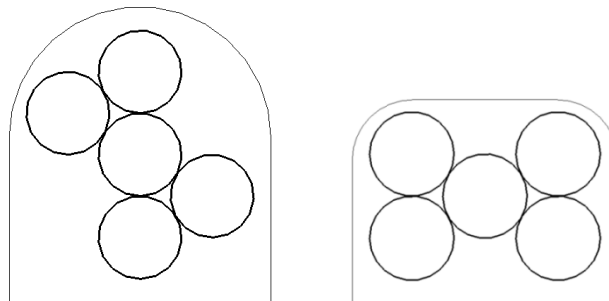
(Izquierda) posición engranajes diferencial versión preliminar. (Derecha) posición engranajes diferencial versión definitiva.
